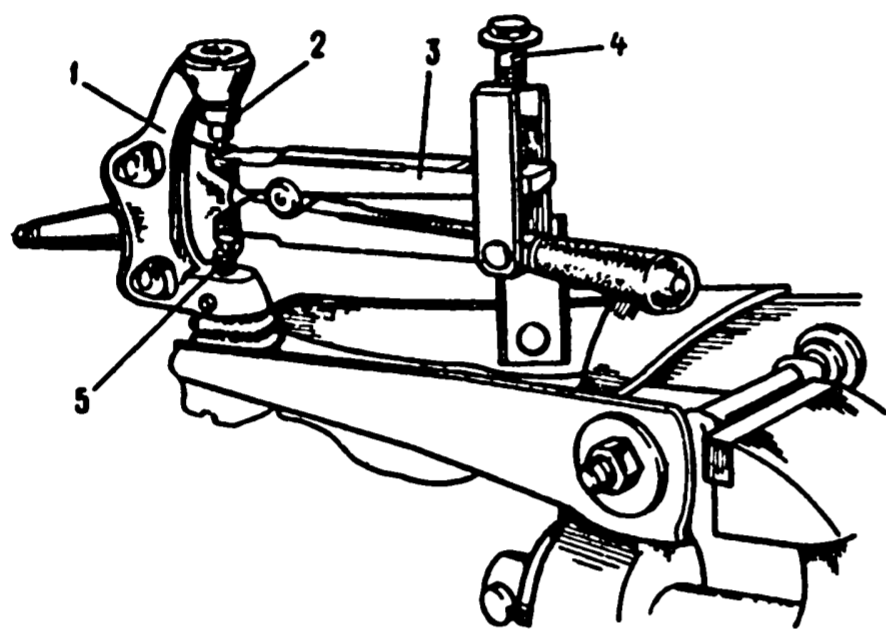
Отсоединение нижнего рычага: 1 - поворотный кулак; 2 - упор; 3 - приспособление 67.7801.951; 4 - болт; 5 - палец шарового шарнира
